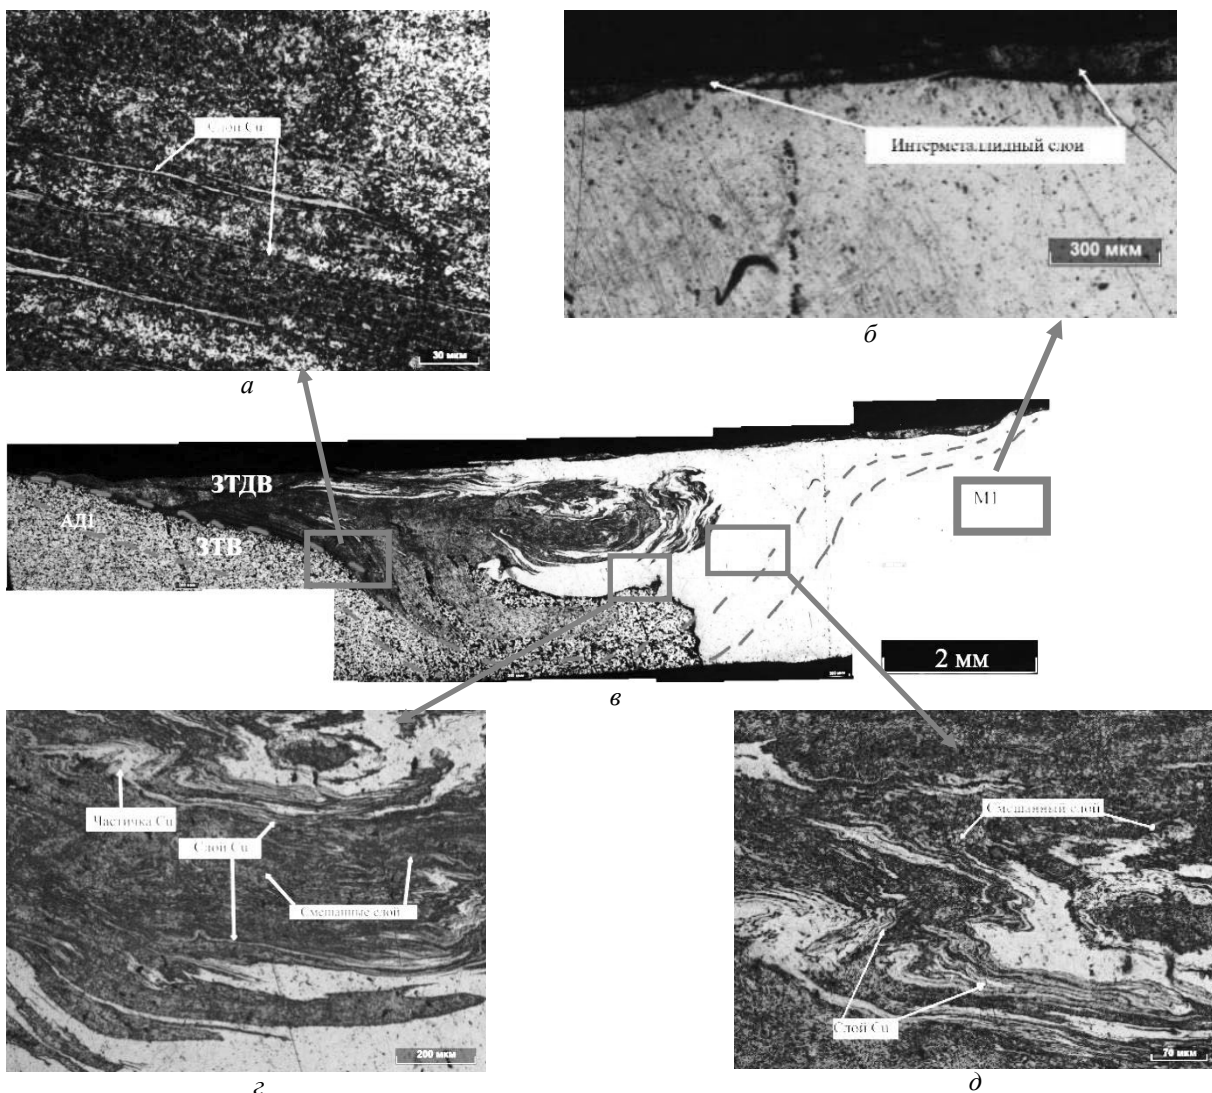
Макрошлиф сварного шва алюминиевого и медного сплава (режим 5)
